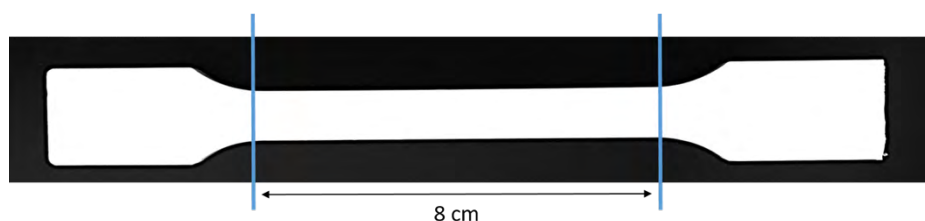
Zuschnitt der Messprobekörper für den Biegeversuch aus einer Zugstabprobe.
